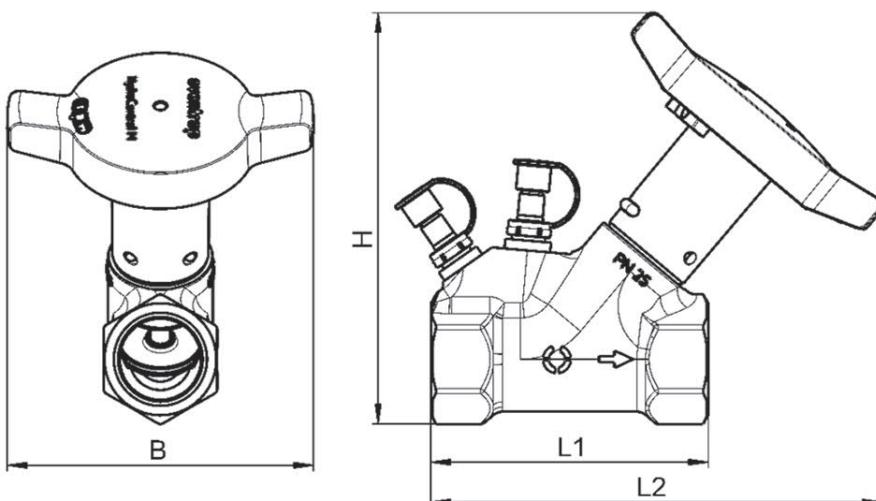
Abmessungen Seitenansicht / Frontansicht Innengewinde
